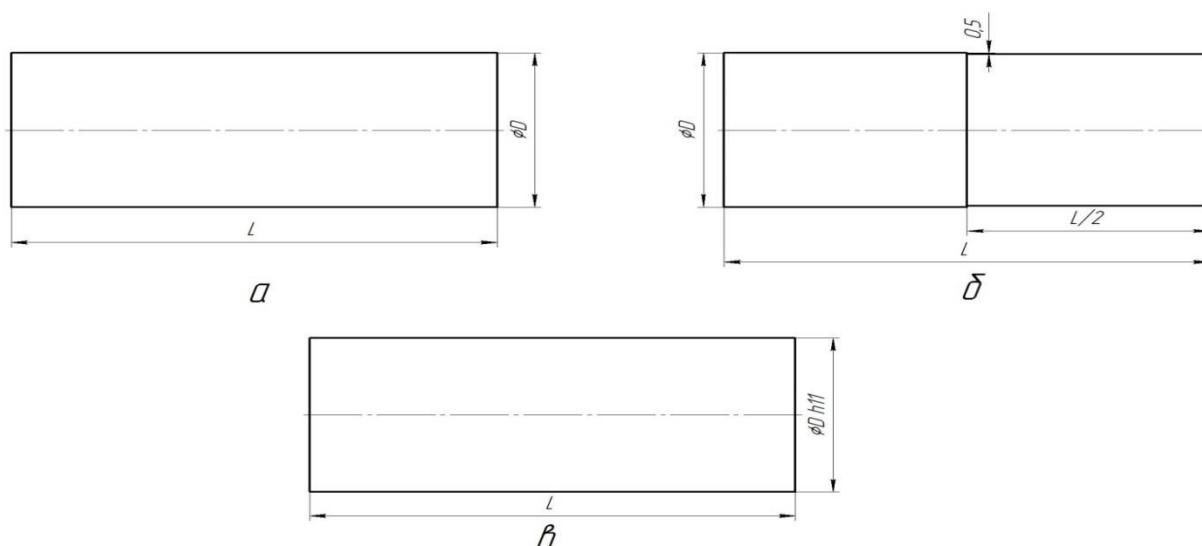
Типы используемых заготовок: а – по ГОСТ 2590, б – частично обточенный из заготовки ГОСТ 2590; в – по ГОСТ 14955-77 по h11 качеству
